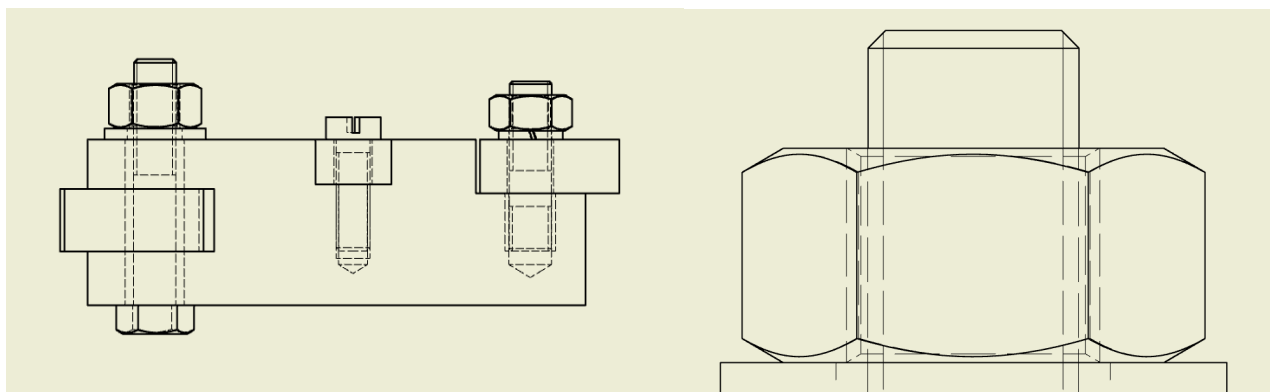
Главный вид резьбовых соединений в разрезе на чертеже и с увеличенным масштабом
